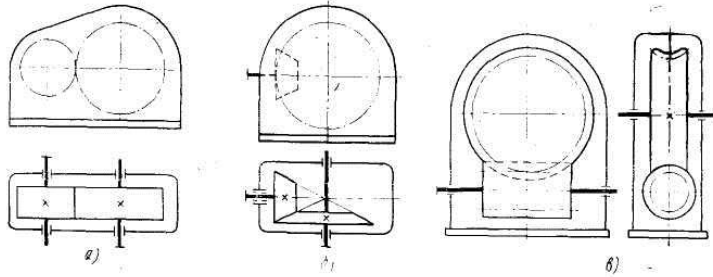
Схемы редукторов: а — одноступенчатый с цилиндрическими колесами, б — одноступенчатый с коническими колесами, в — одноступенчатый червячный
